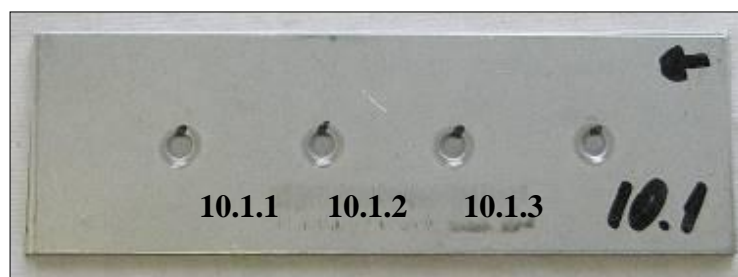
Внешний вид точечной контактной сварки образца № 10.1
